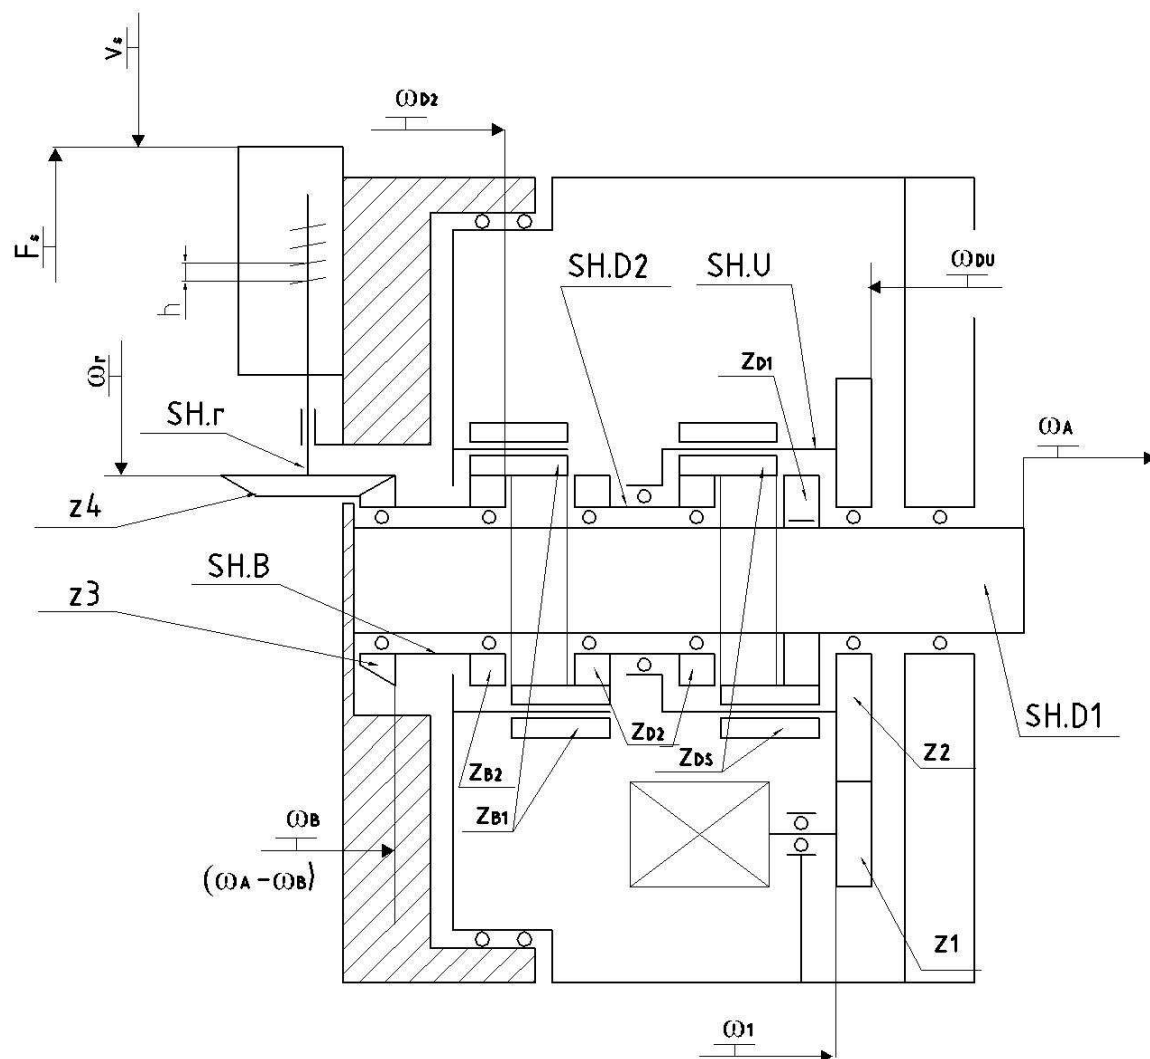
Frézovací zařízení se dvěma řízenými souřadnicemi se sklonem os 45° [3]
